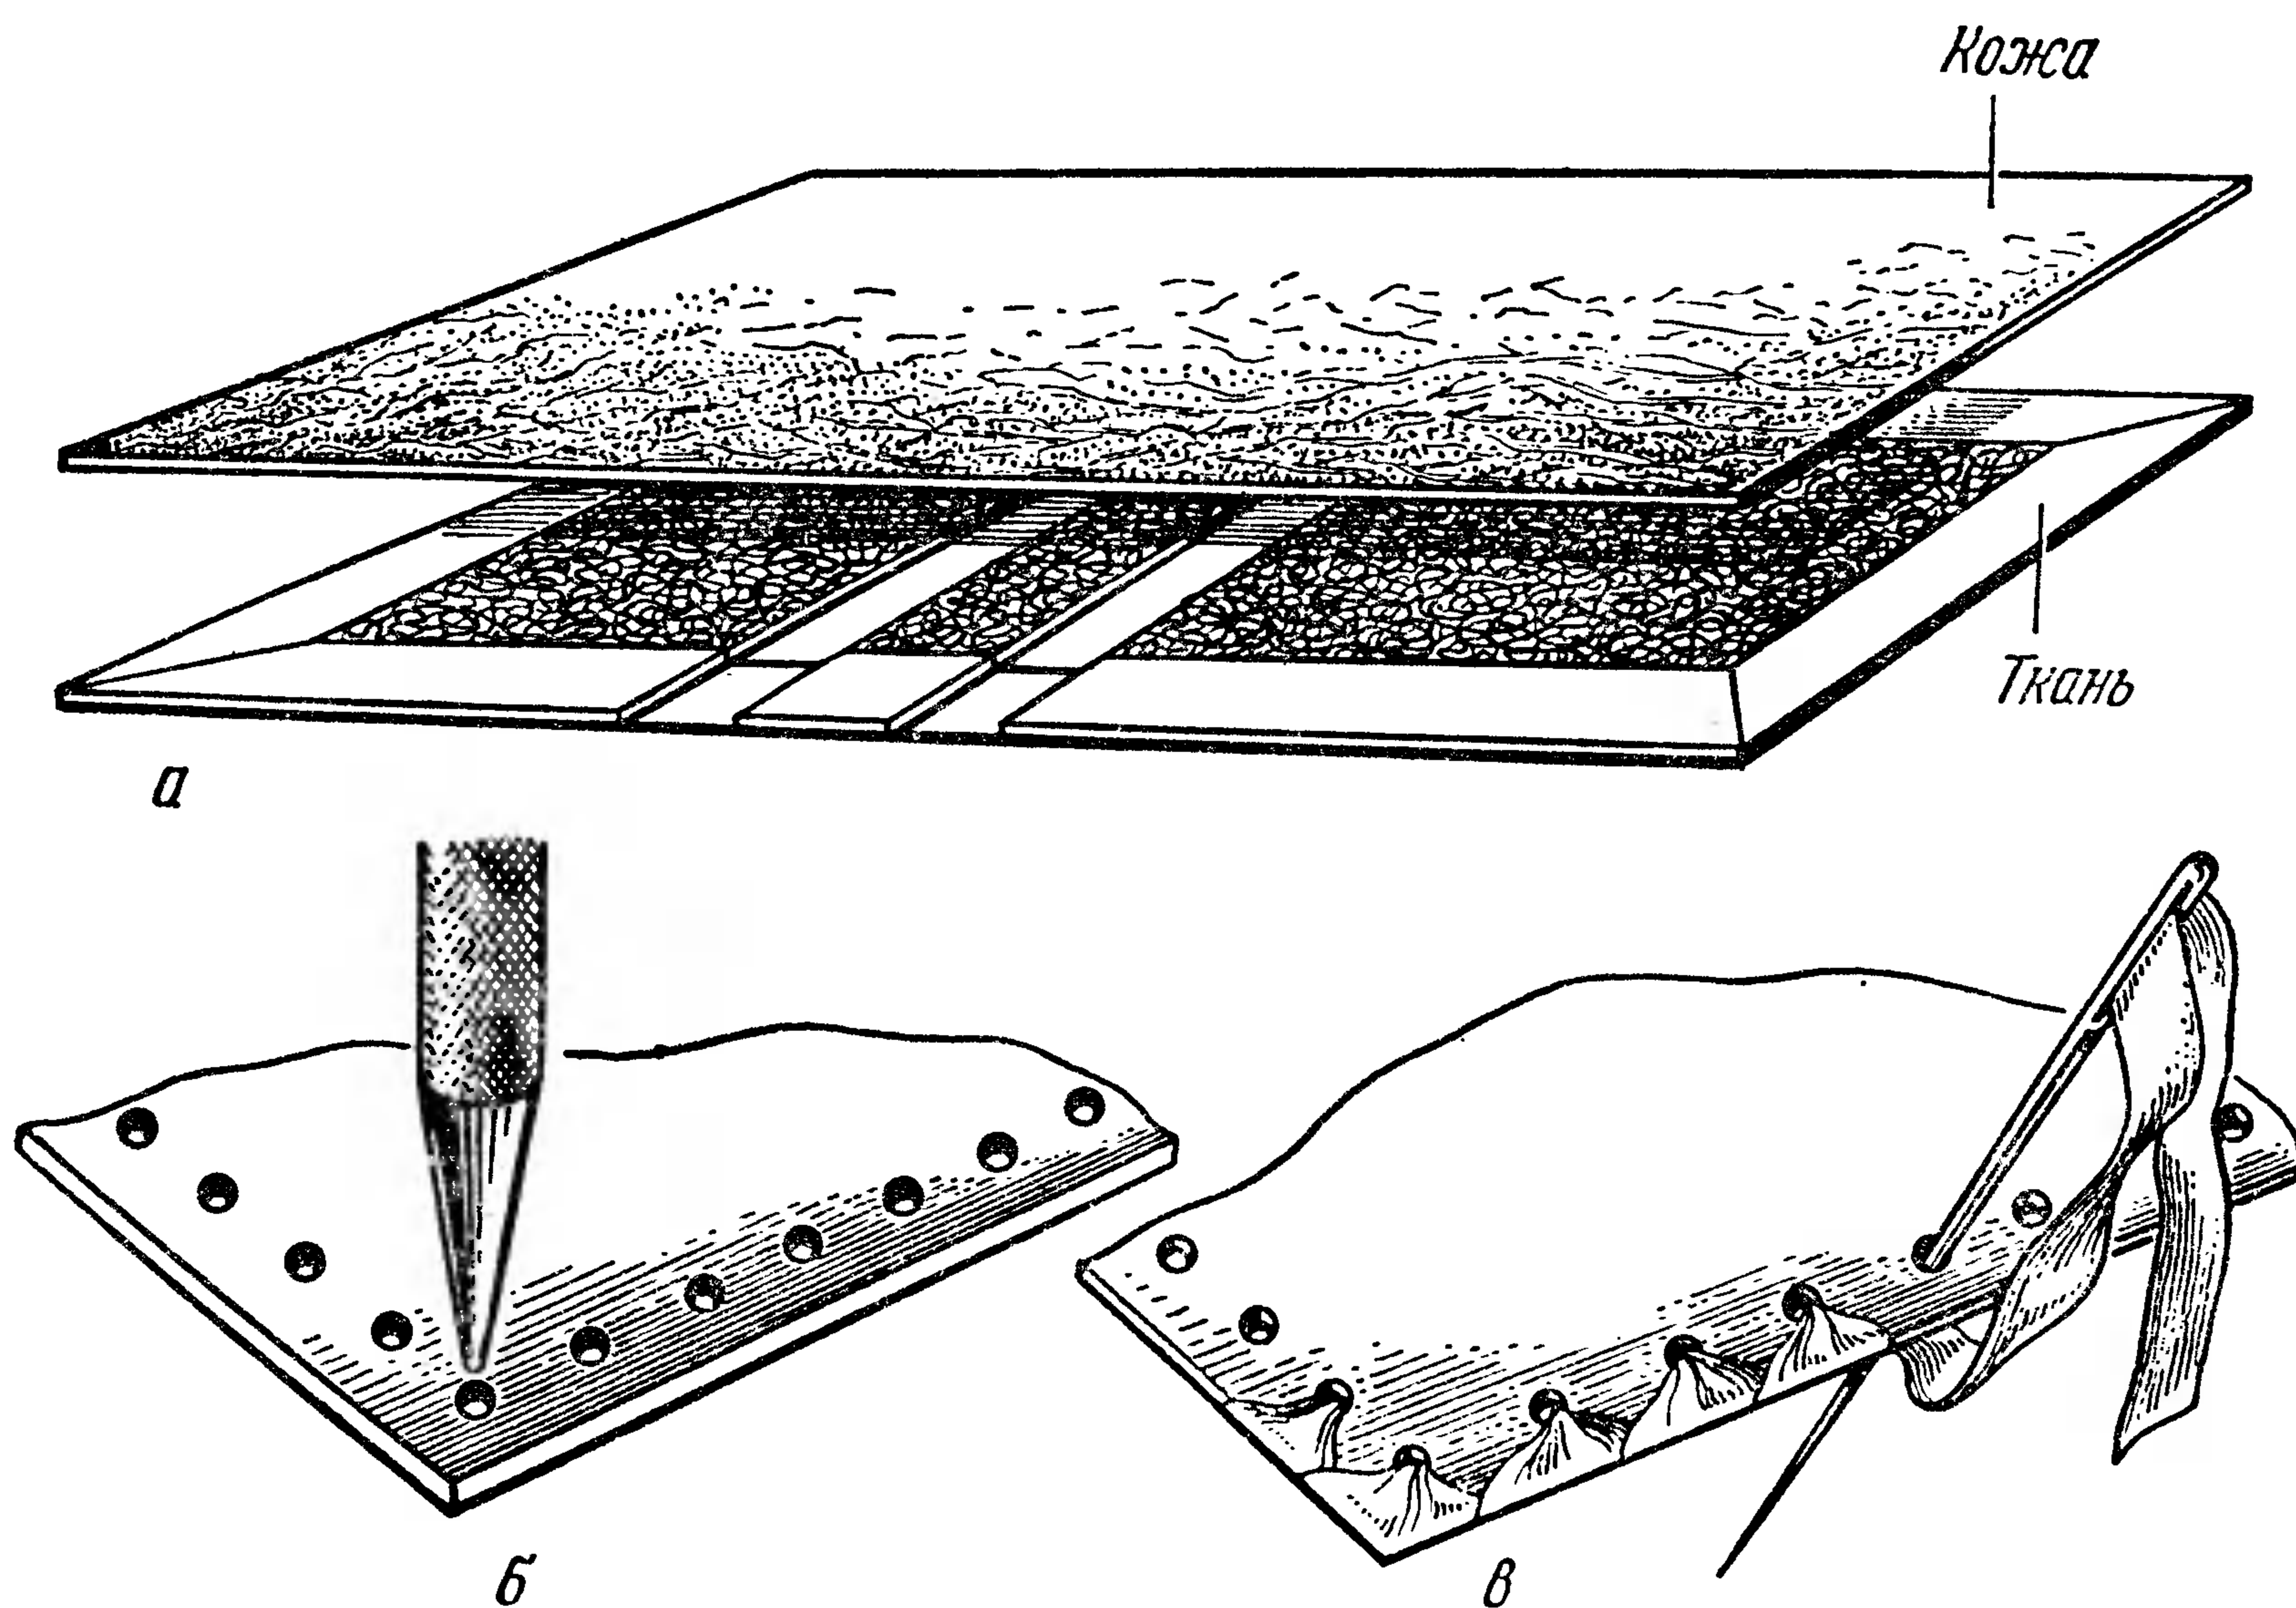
Изготовление кожаной крышки для альбома: а — схема расположения деталей; б — пробивка отверстий на кромках; в — обшивка крышки.
